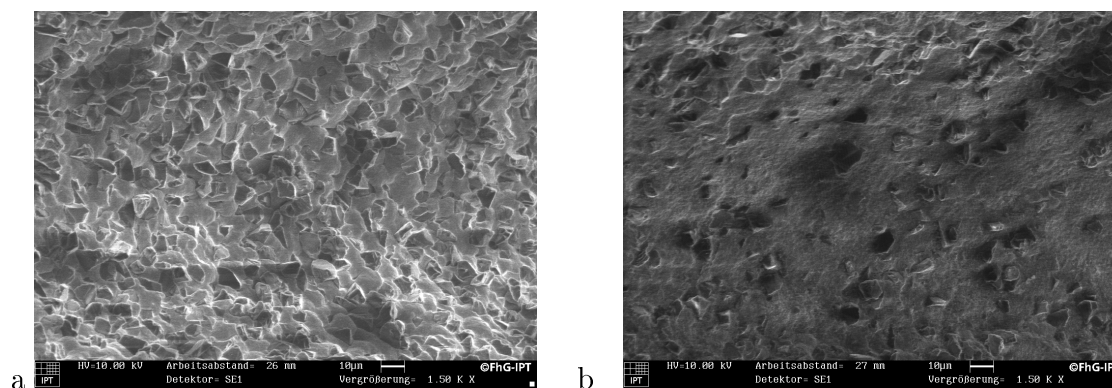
a) Neue Abriebschicht eines einschichtig belegten Werkzeuges. b) Abgenutzte Abriebschicht eines einschichtig belegten Werkzeuges. Die Schleifkörner sind aus der Bindung gebrochen.
